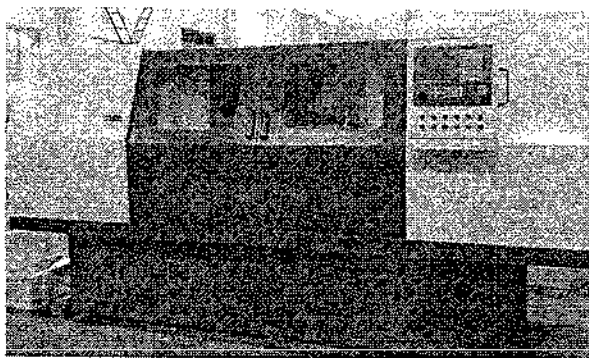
Фрезерно-центровальный станок с ЧПУ XZK 8230-3000
